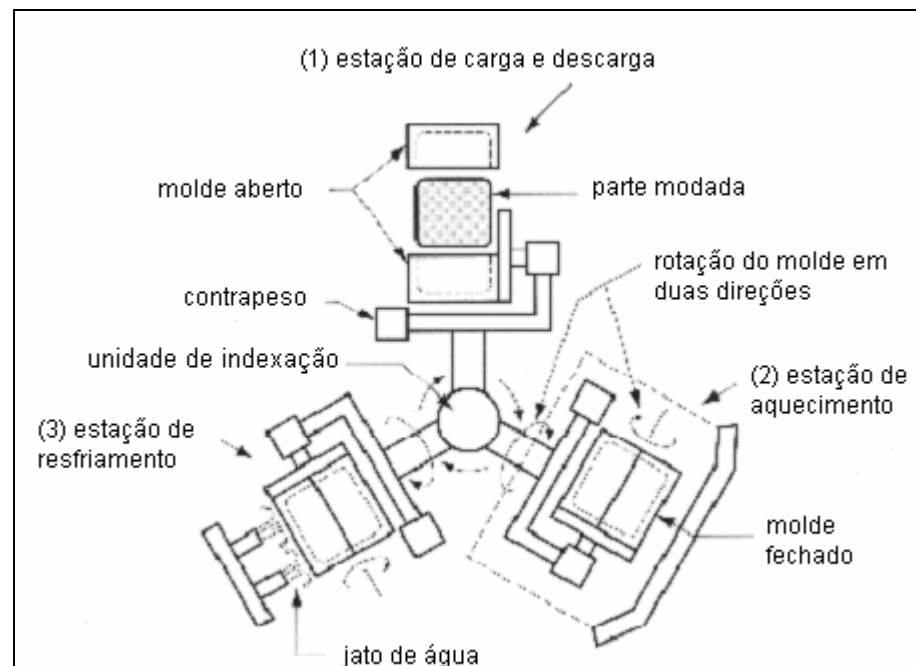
Ciclo de moldagem rotacional em máquina de três estações: (1) carga e descarga, (2) aquecimento e rotação do molde e (3) resfriamento do molde (PLASTUNIVERS-1997).
